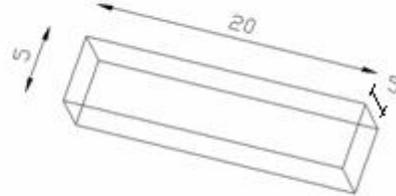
Probeta para ensayo de compresión con deformímetro
